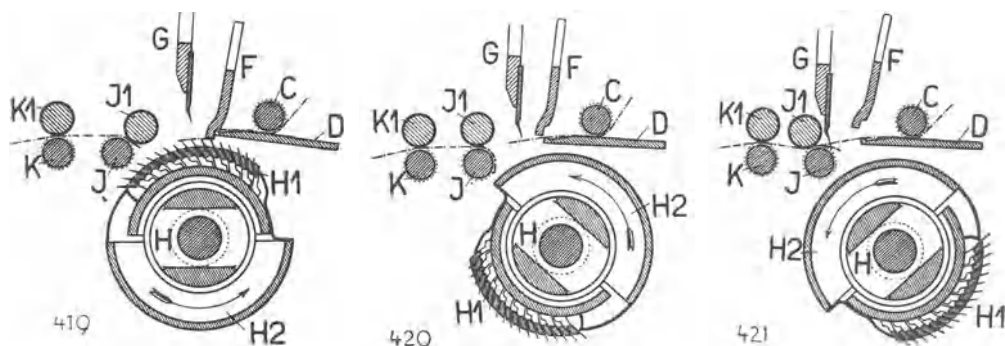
bis 221. Einzelheiten zur Flachkämmaschine.
